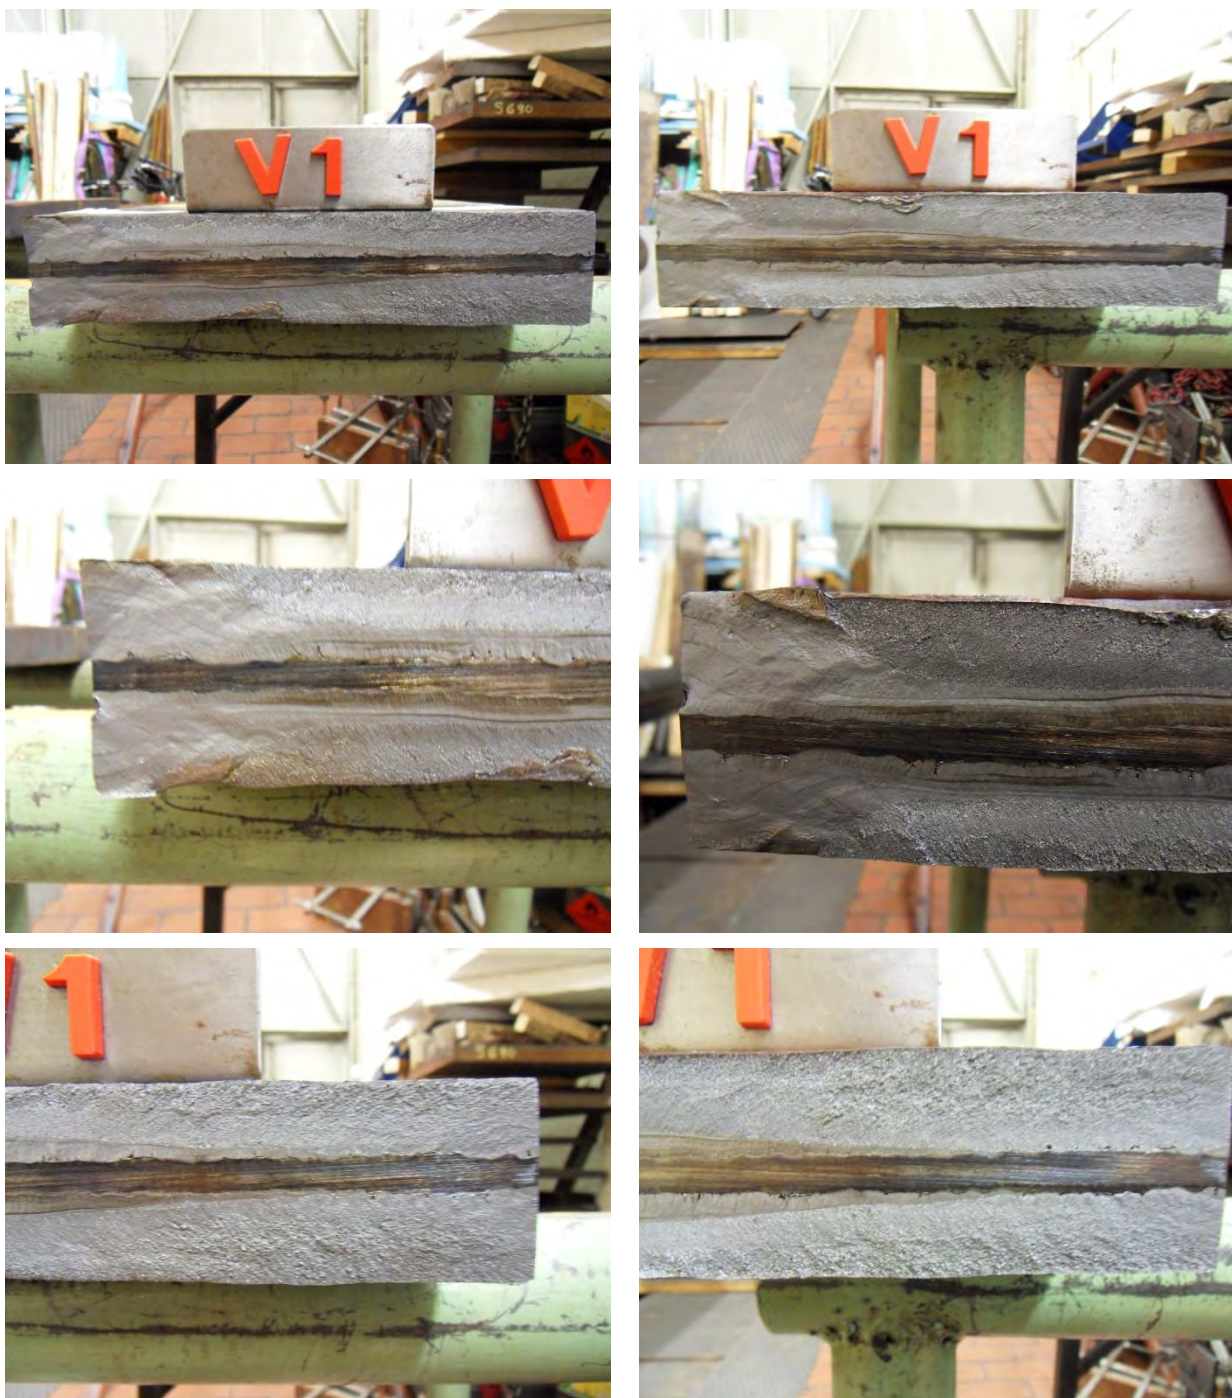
Bruchflächen / Bruchbild des Stumpfstoßes DHY-N6-2
